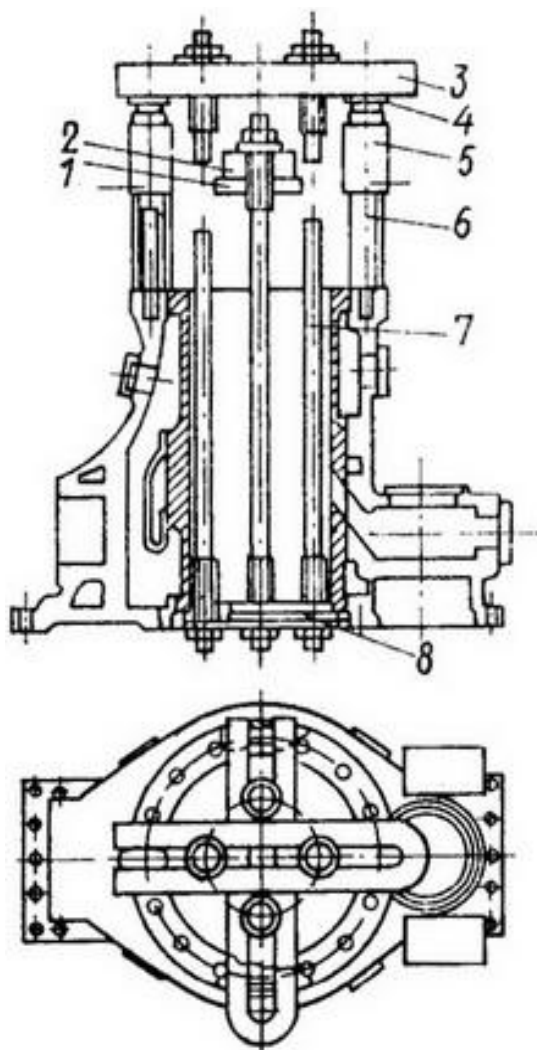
Приспособление для гидравлической выпрессовки втулок
